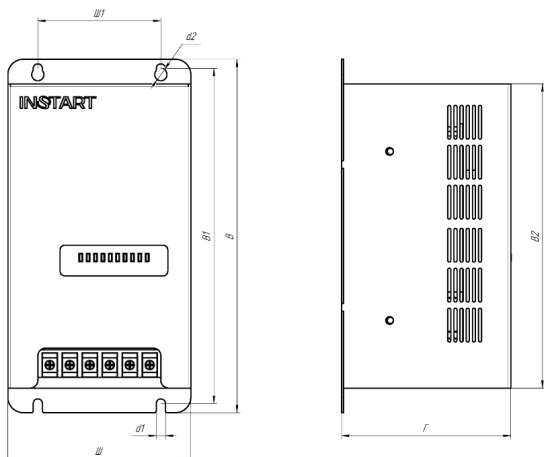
Установочные и габаритные размеры тормозного модуля FCI-BU, типоразмер 1
